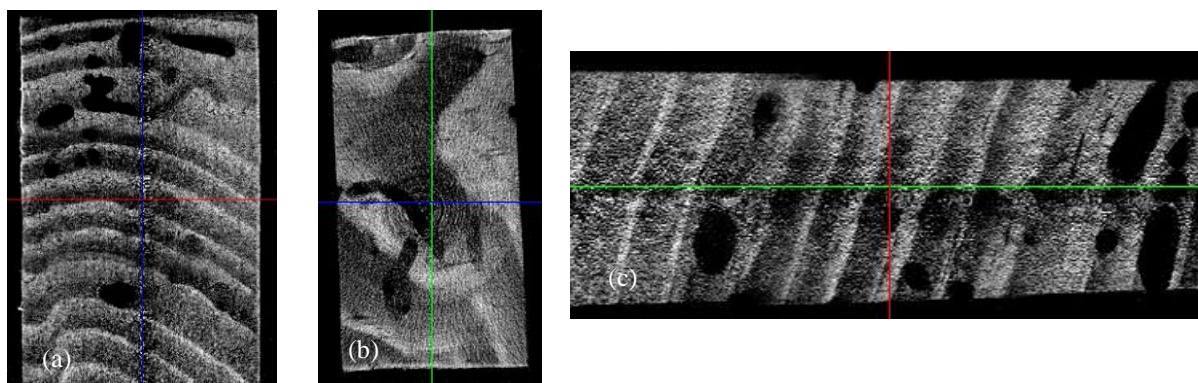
Imagens 2D do objeto reconstruído: (a) plano coronal; (b) plano sagital; (c) plano transaxial.
